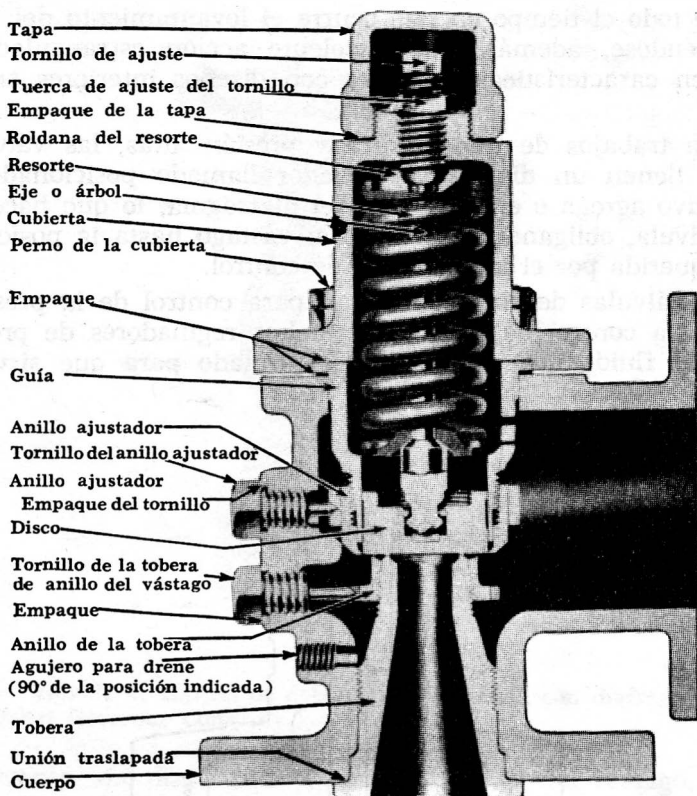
Válvula de desahogo. (Cortesía de Crosby Steam Gage and Valve Company.)
